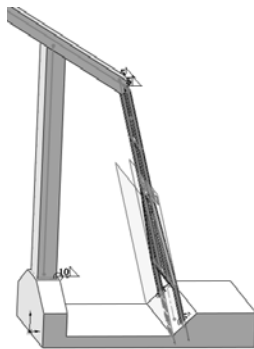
创建半径为 5.00mm 的焊缝
